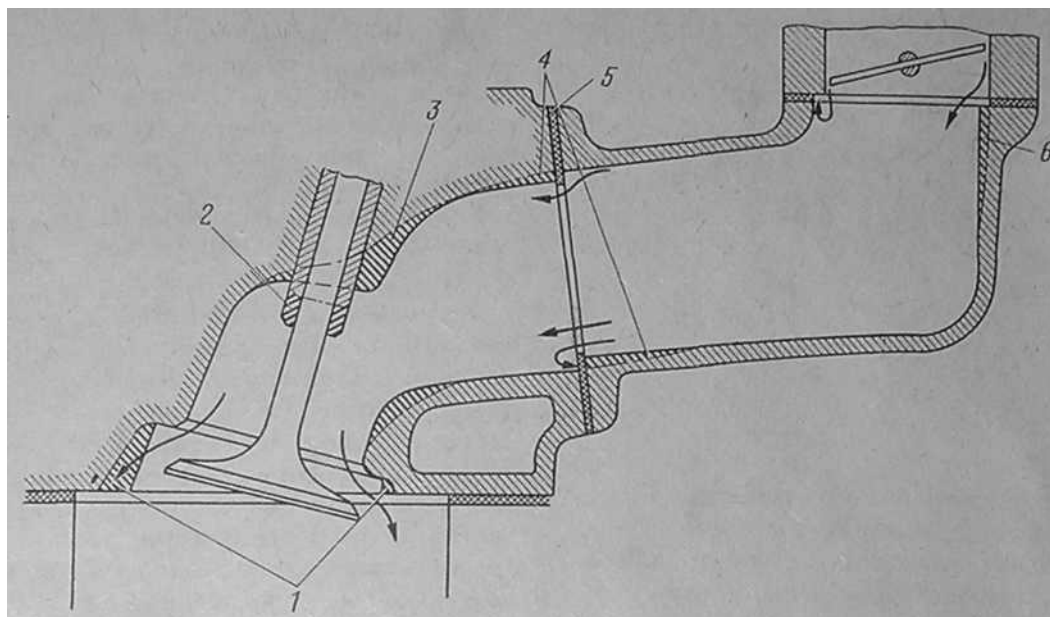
Схема обработки впускного канала и камеры сгорания: 1 – обработка камеры сгорания; 2 – уменьшение выступающей части направляющей втулки клапана; 3 – обработка средней части впускного канала; 4 – обработка несовпадающих частей впускного канала в месте соединения впускного трубопровода и головки блока цилиндров; 5 – прокладка; 6 – обработка впускного канала под карбюратором.
